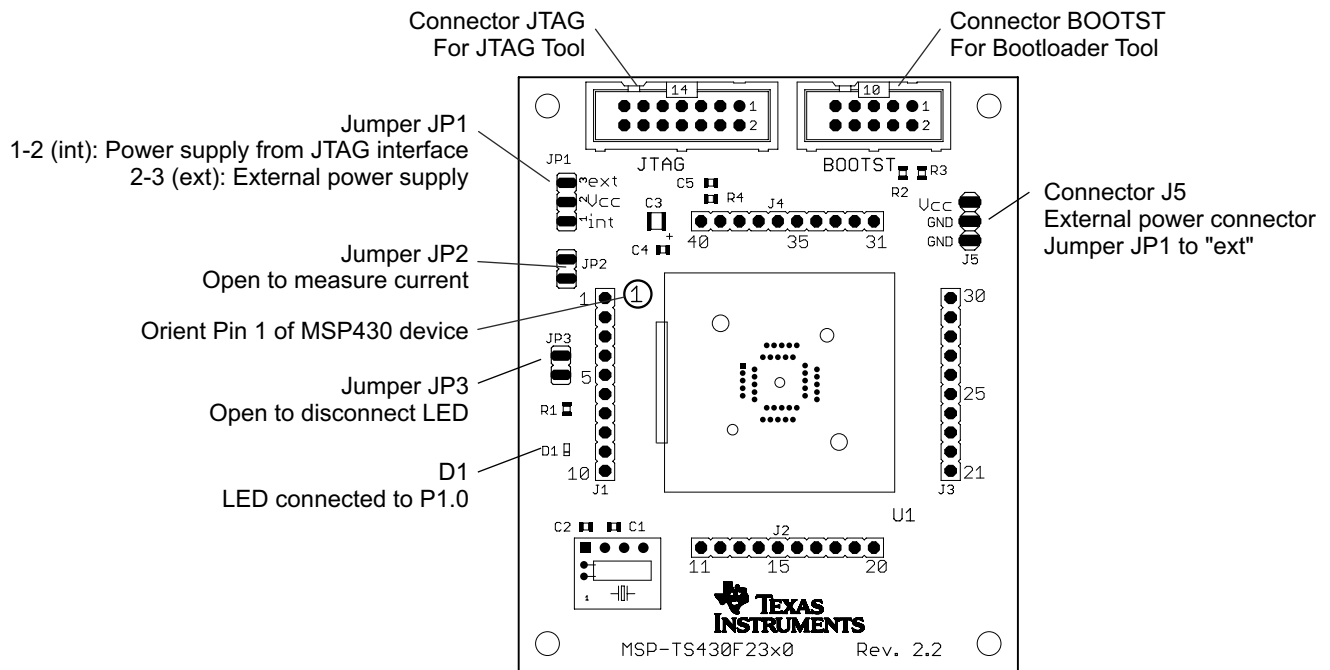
MSP-TS430QFN23x0 目标插座模块、PCB
